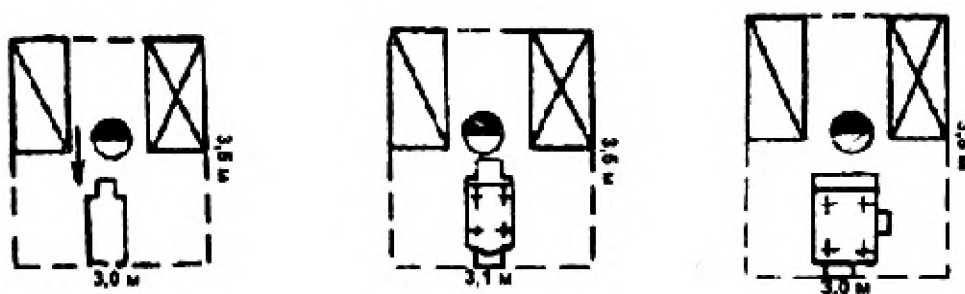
Условное обозначение шипорезных станков СВП-2, СВА, СВПА-2
